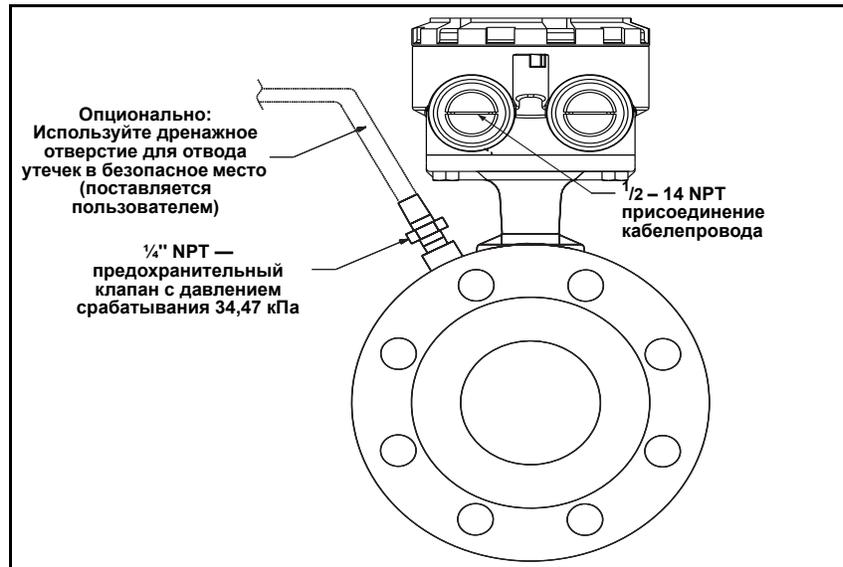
Стандартное исполнение корпуса — герметичный сварной корпус (Код варианта W0)
